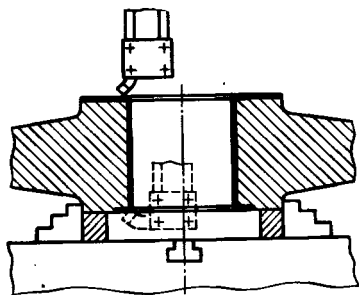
Схема установки диска под окончательное точение ступицы на карусельном станке
